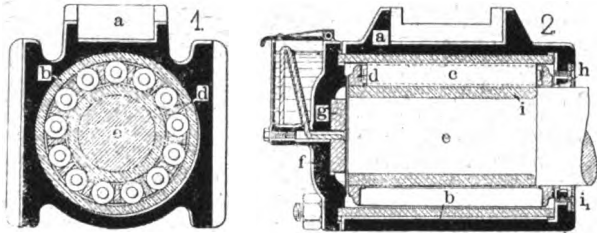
Rollenlager der British Roller Bearings Co. in Westminster.
